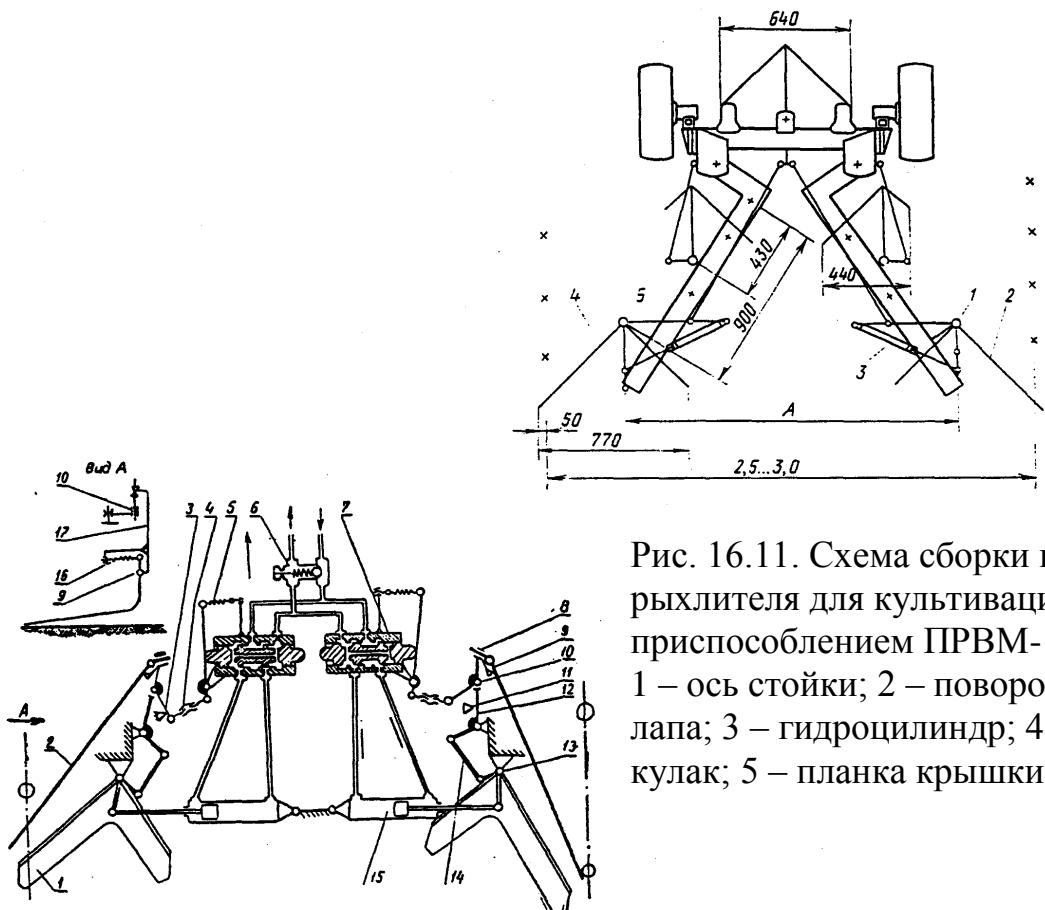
Схема сборки плуга рыхлителя для культивации с приспособлением ПРВМ-11.000:
